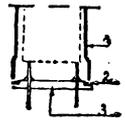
Assemblage de l'ampoule et de la plaque de fond.
